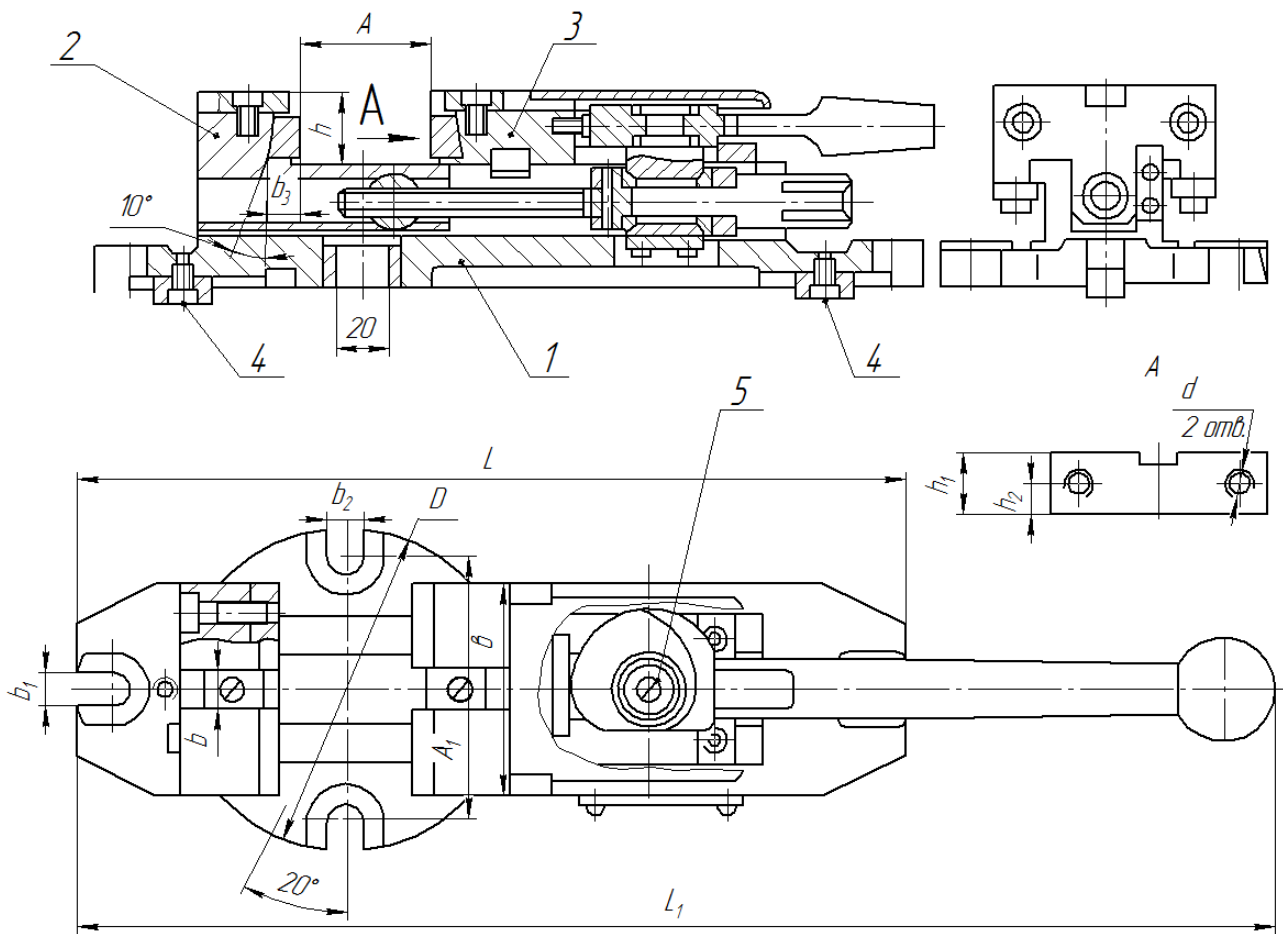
Будова й параметри лещат верстатних з ексцентриковим затискачем та однією рухомою губкою (ГОСТ 18237-72): 1 – корпус; 2 – нерухома губка; 3 – рухома губка; 4 – шпонка; 5 – ексцентриковий механізм
